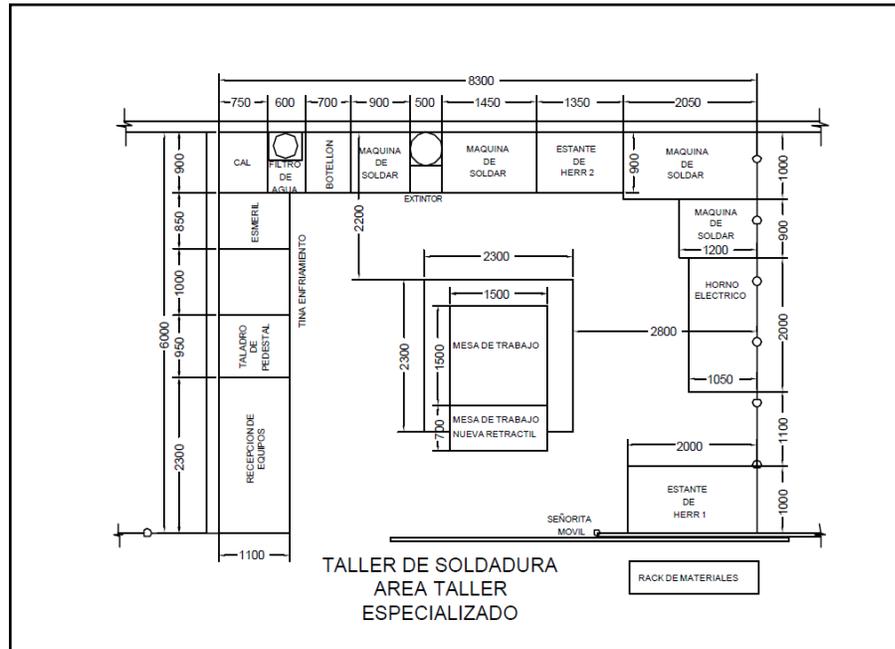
Distribución Propuesta en planta del Taller de Soldadura
